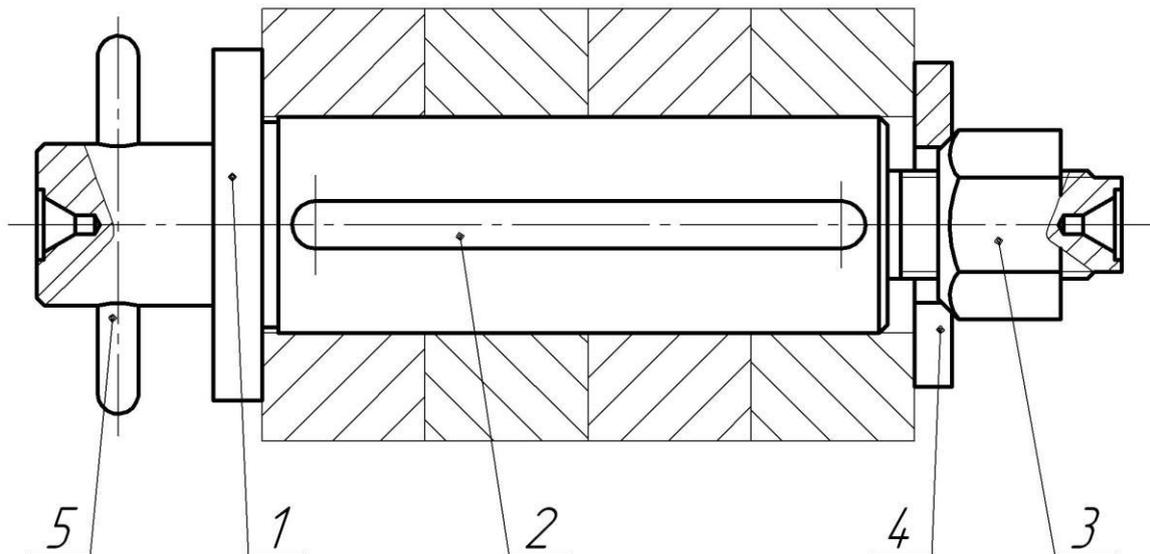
Цилиндрическая оправка для посадки заготовки с гарантированным зазором
